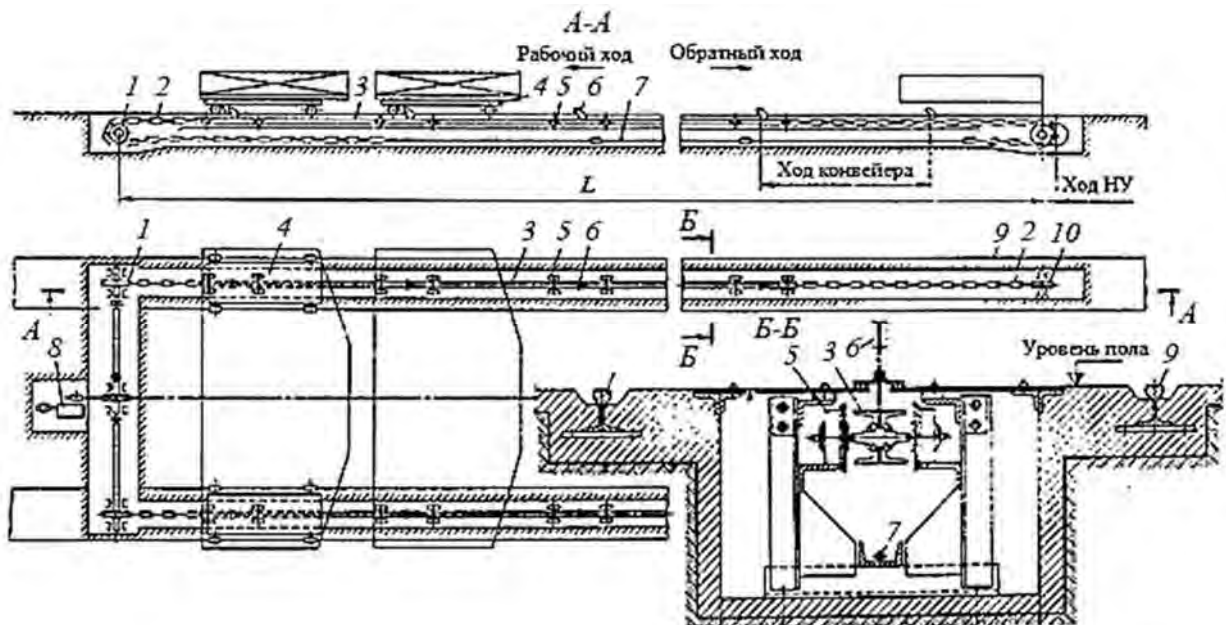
Схема грузоведущего двухштангового конвейера: 1 – приводная звездочка; 2 – цепь (канат); 3 – штанга; 4 – тележка; 5 – опорные катки; 6 – ведущие толкатели; 7 – тяга; 8 – привод; 9 – рельсовый путь; 10 – натяжная звездочка
